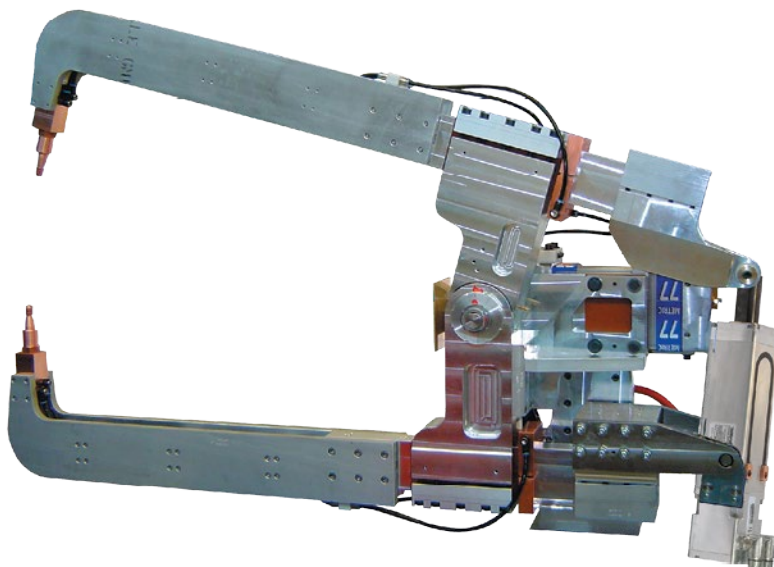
Ejemplo de actuador ServoWeld instalado en la unidad de pistola de soldar estilo "X".
